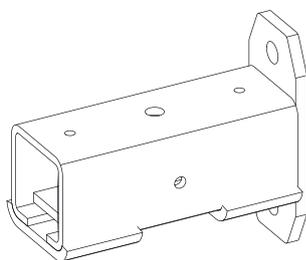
Support à visser avec une plaque de raccordement à 2 trous (acier, galvanisé)
